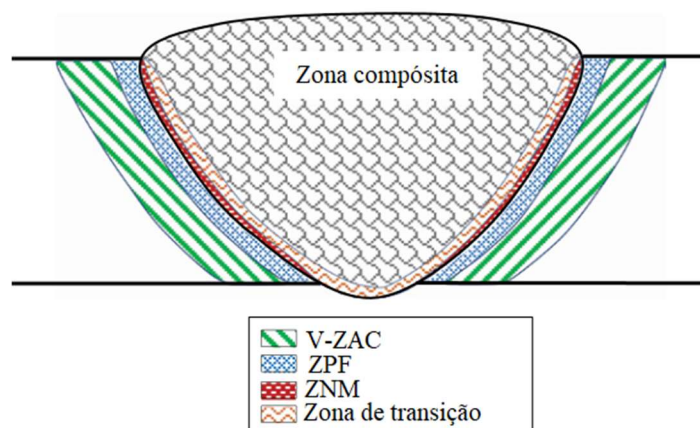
Zona de transição em soldadura com material base distinto do material de adição [22]
